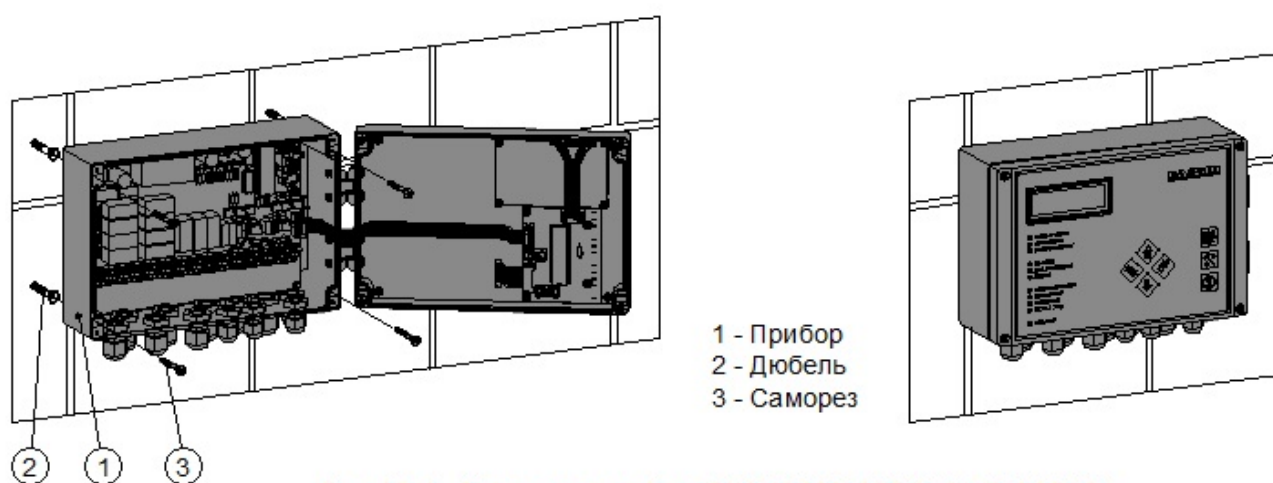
Установка прибора СТАНДАРТ / ПРОФИ / МАСТЕР
